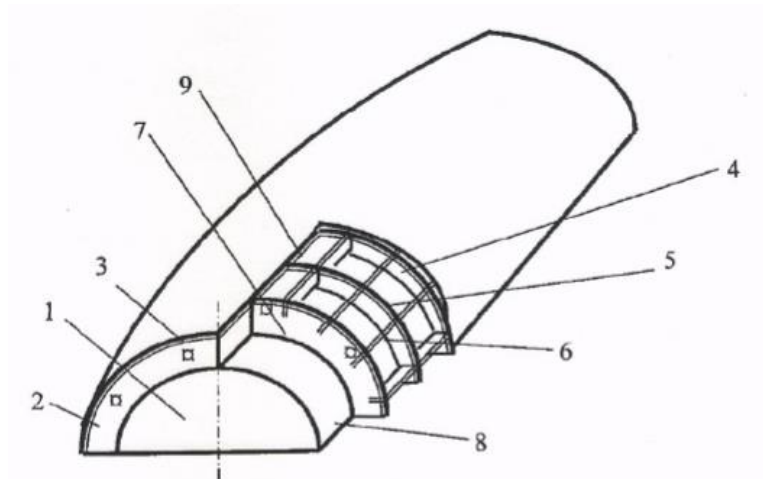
Обтяжной пуансон со сменной рабочей поверхностью-накладкой, устанавливаемый на опору: 1 – опора; 2 – накладка; 3 – обшивка; 4 – ячейки; 5 – поперечный набор пластин; 6 – продольный набор пластин; 7 – внутренняя поверхность накладки 2; 8 – рабочая поверхность опоры 1; 9 – наружная поверхность накладки 2
